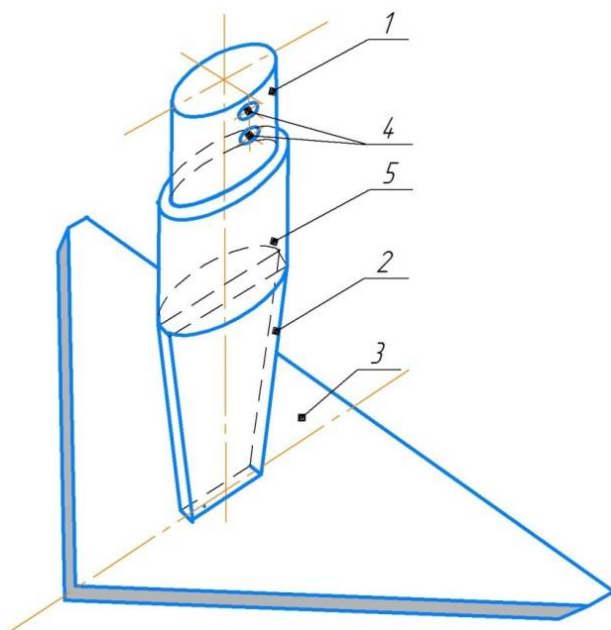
Общий вид рабочего органа почвообрабатывающей фрезы
